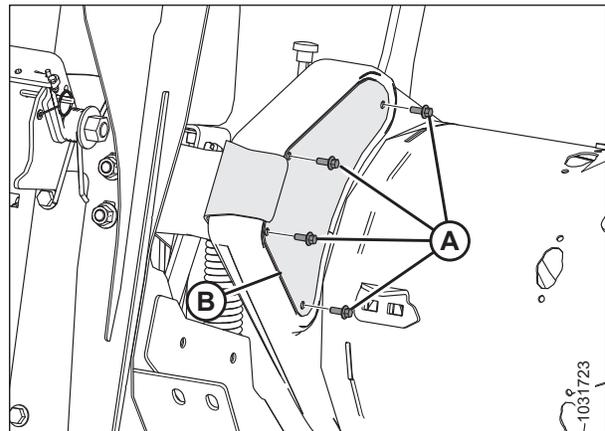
Linke Seite des Einzugsschnecke-Getriebes – Rückansicht
